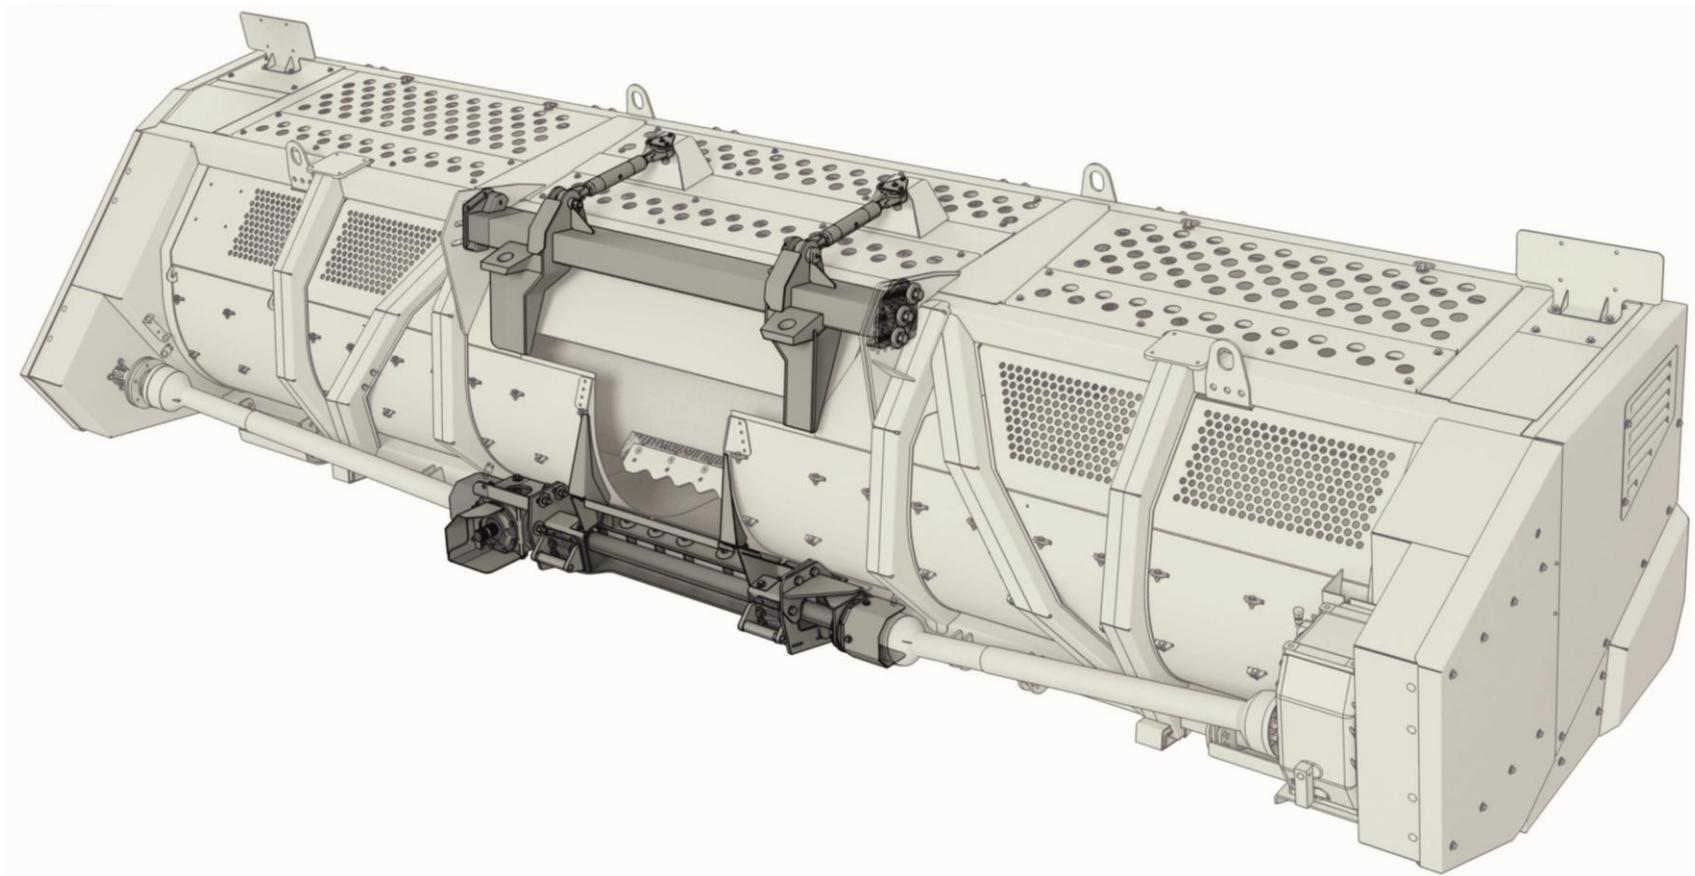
Установка рамы ЖРН-605.02.00.000Б
